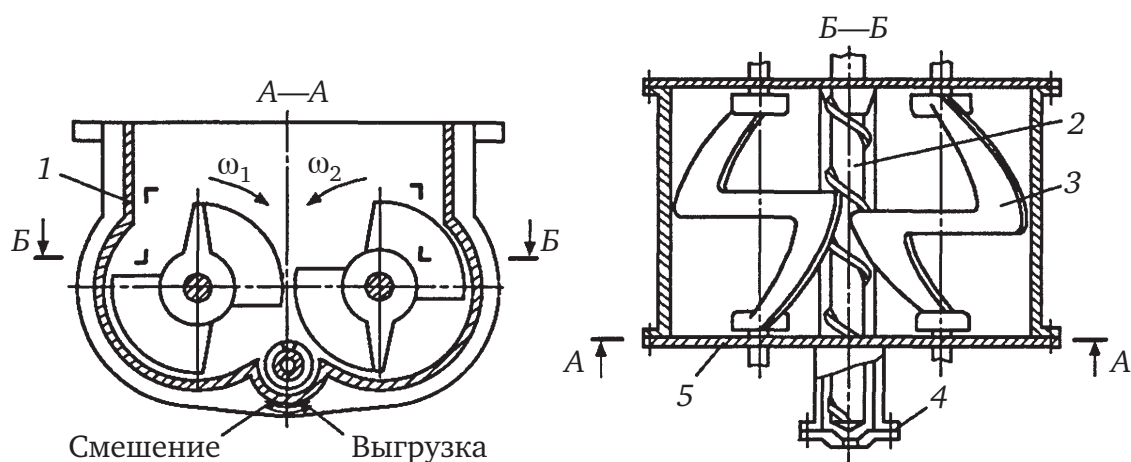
Двухроторный смеситель с реверсивным червяком
